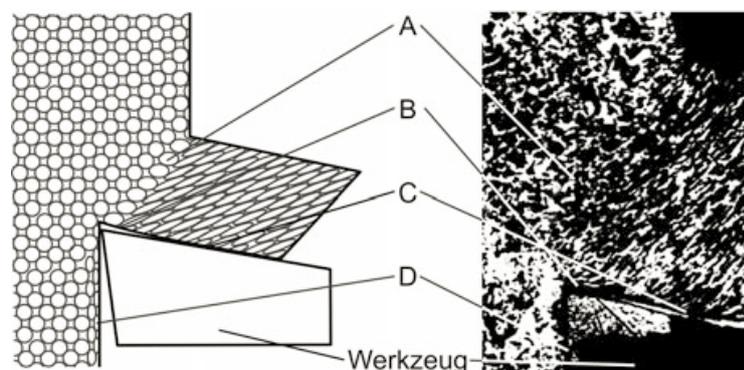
Spanbildung und Spanstruktur; Quelle: Zerspanung der Eisenwerkstoffe, Stahleisen-Bücher
